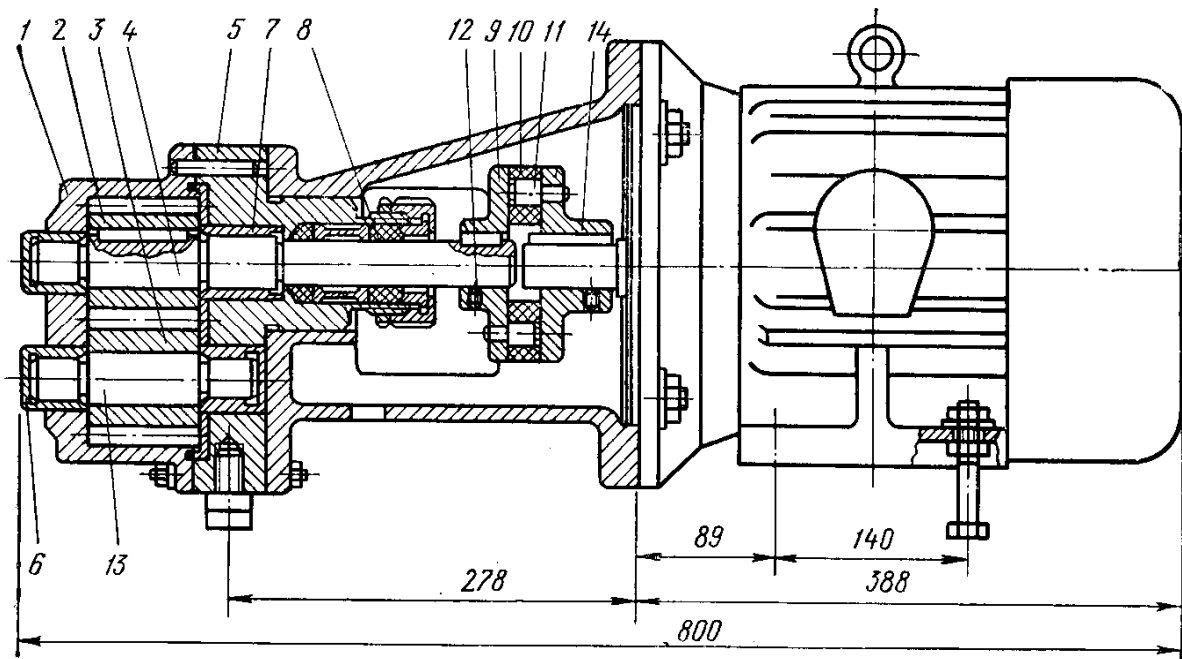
Насос НШМ-5: 1 – корпус; 2 – ведуча шестерня; 3 – ведена шестерня; 4 – ведучий вал; 5 – основа; 6, 7 – бронзові втулки; 8 – ущільнювальна набивка; 9 – ведена напівмуфта; 10 – кільце; 11 – палець муфти; 12 – кріпильний гвинт; 13 – вал веденої шестерні; 14 – ведуча напівмуфта.
